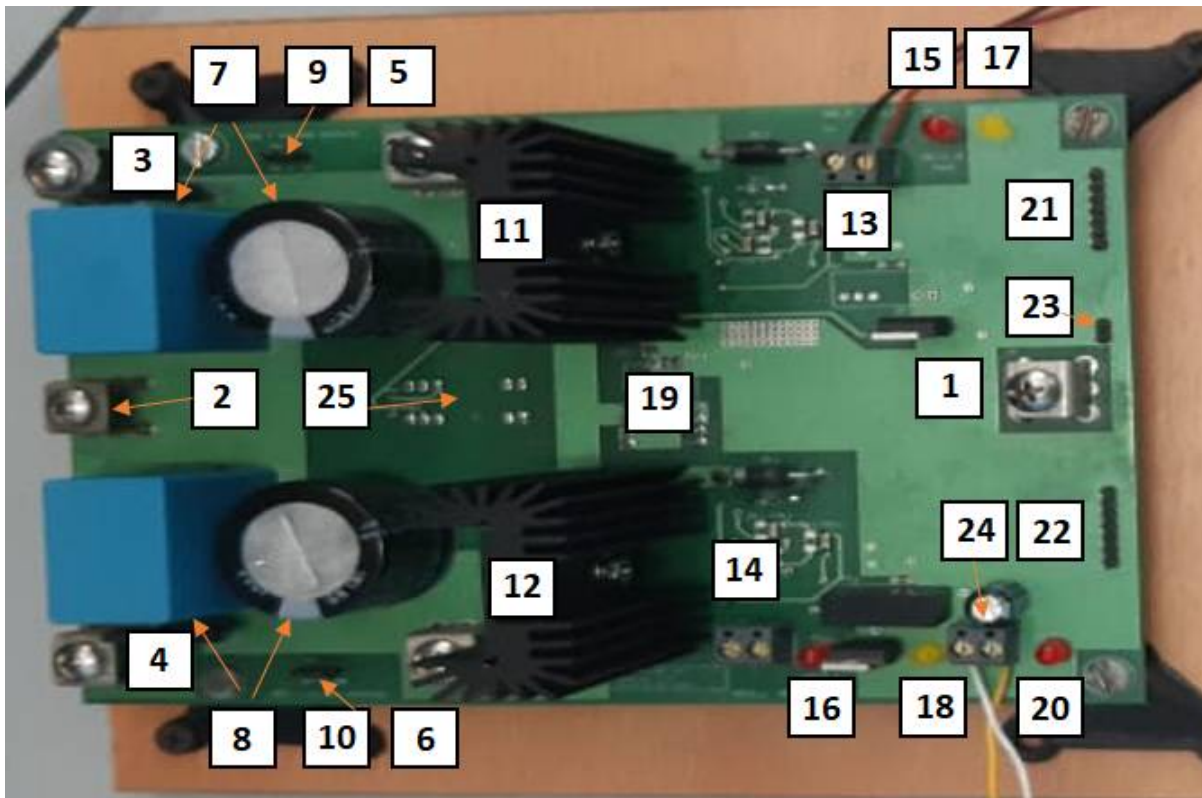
Placa de circuito impreso: Capa superior. Componentes soldados. Referencias.
